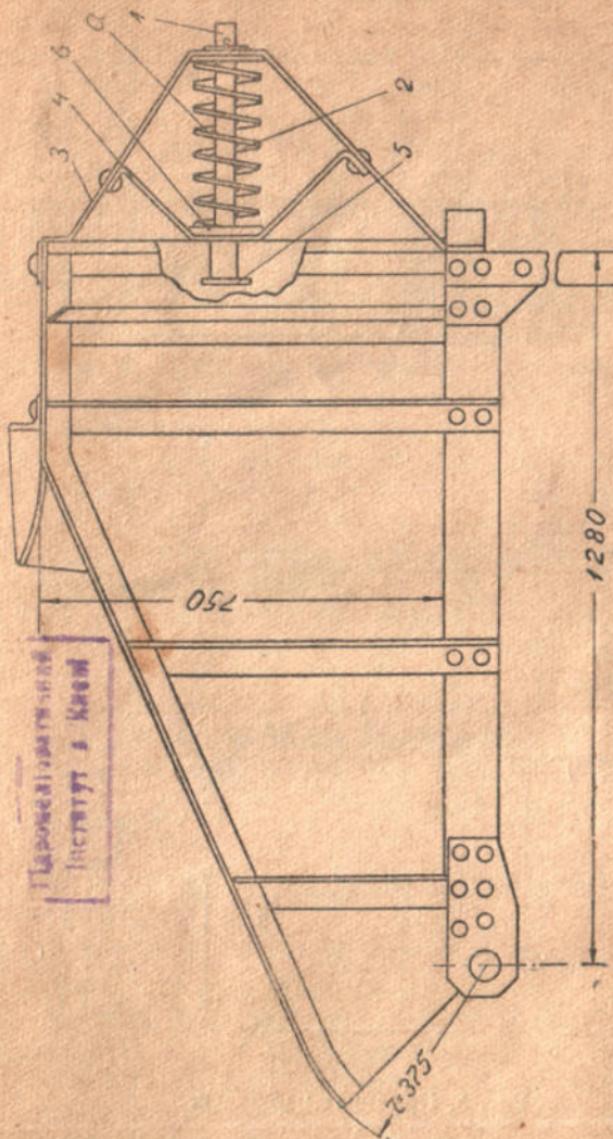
Разгрузочная площадка: 1 — скалка; 2 — пружина; 3 — упорная скоба; 4 — направляющая скоба; 5 — буфер; 6 — тарелка.
